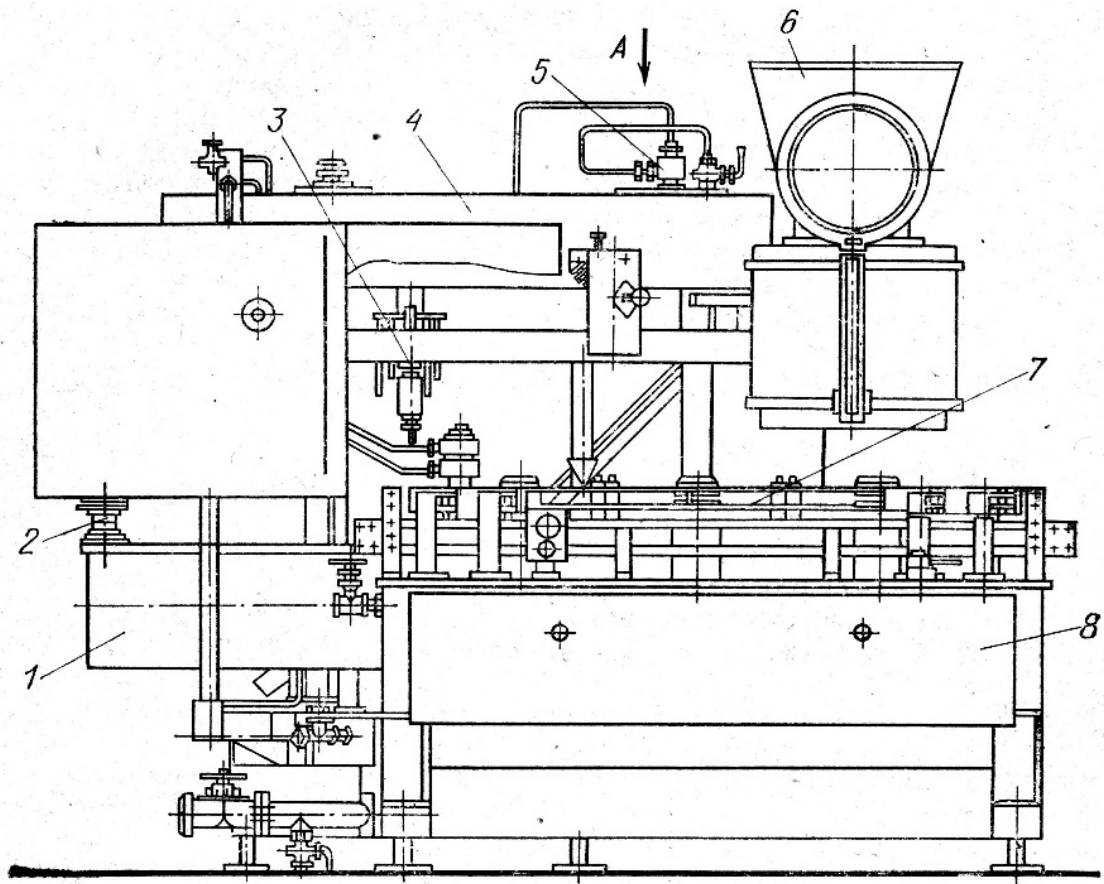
Розливочно-закупорювальний блок марки РЗ-ВМБ-40/6:
